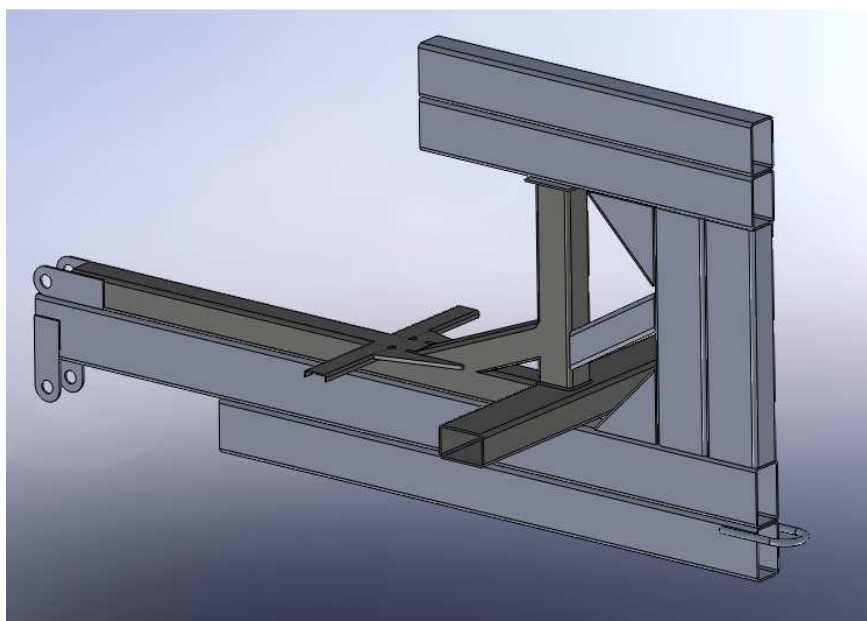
Estrutura de apoio ao ensaio de fecho da ligação pilar-estrado
